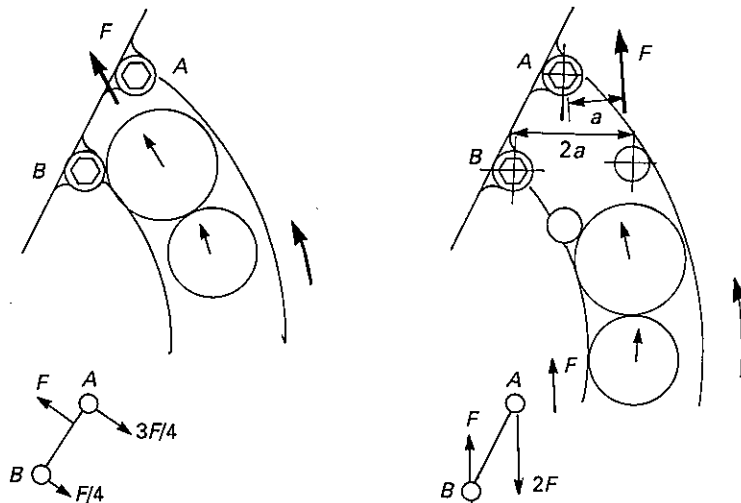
Durch Versetzen der Bremszange können sich die Kräfte in den Befestigungsschrauben drastisch ändern. In diesem Fall steigt die Kraft in der oberen Befestigungsschraube um das 2,67-fache, während die untere Schraube eine um den Faktor vier geringere Kraft aufnehmen muß (bei gleicher Bremskraft). Die Richtung der Kraft hat sich ebenso geändert. Das Gußauge, das die Schraube B hält, wird nun hauptsächlich auf Zug statt auf Druck beansprucht (der Werkstoff ist auf Zug geringer belastbar als auf Druck).
